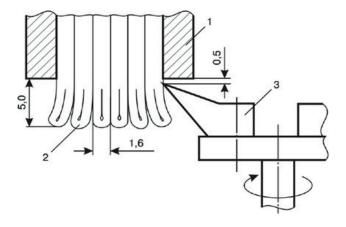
Установка глубины фрезерования корешка блока: 1 - зажим главного транспортера; 2 - блок; 3 - фреза
